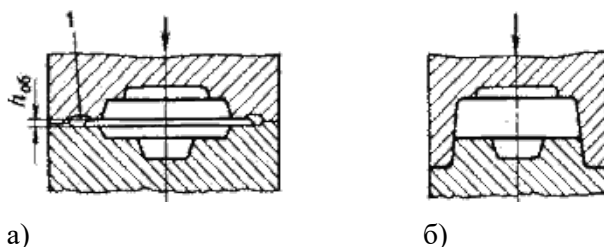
Схемы штамповки в открытых (а) и закрытых (б) штампах:
